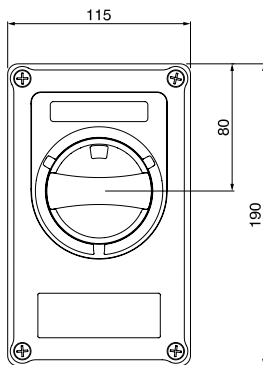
IT: Disegno tecnico / EN: Technical drawing / FR: Dessin technique / ES: Diseño técnico / DE: Technische Zeichnung / NL: Technische tekening
